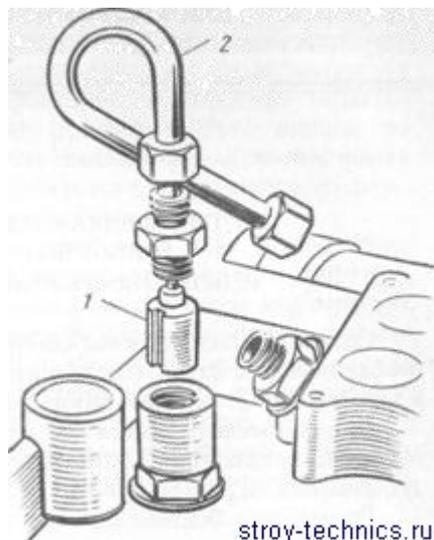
Очистка и промывка клапана вентиляции картера двигателя и трубки двигателя ЗИЛ-Э75ЯТ: 1 — клапан; 2 — соединительная трубка
